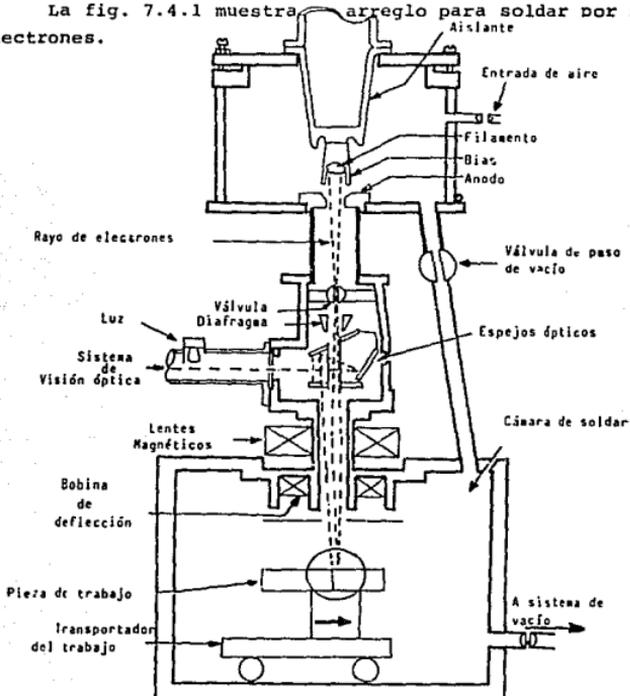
Soldadura por Rayo de Electrones.
